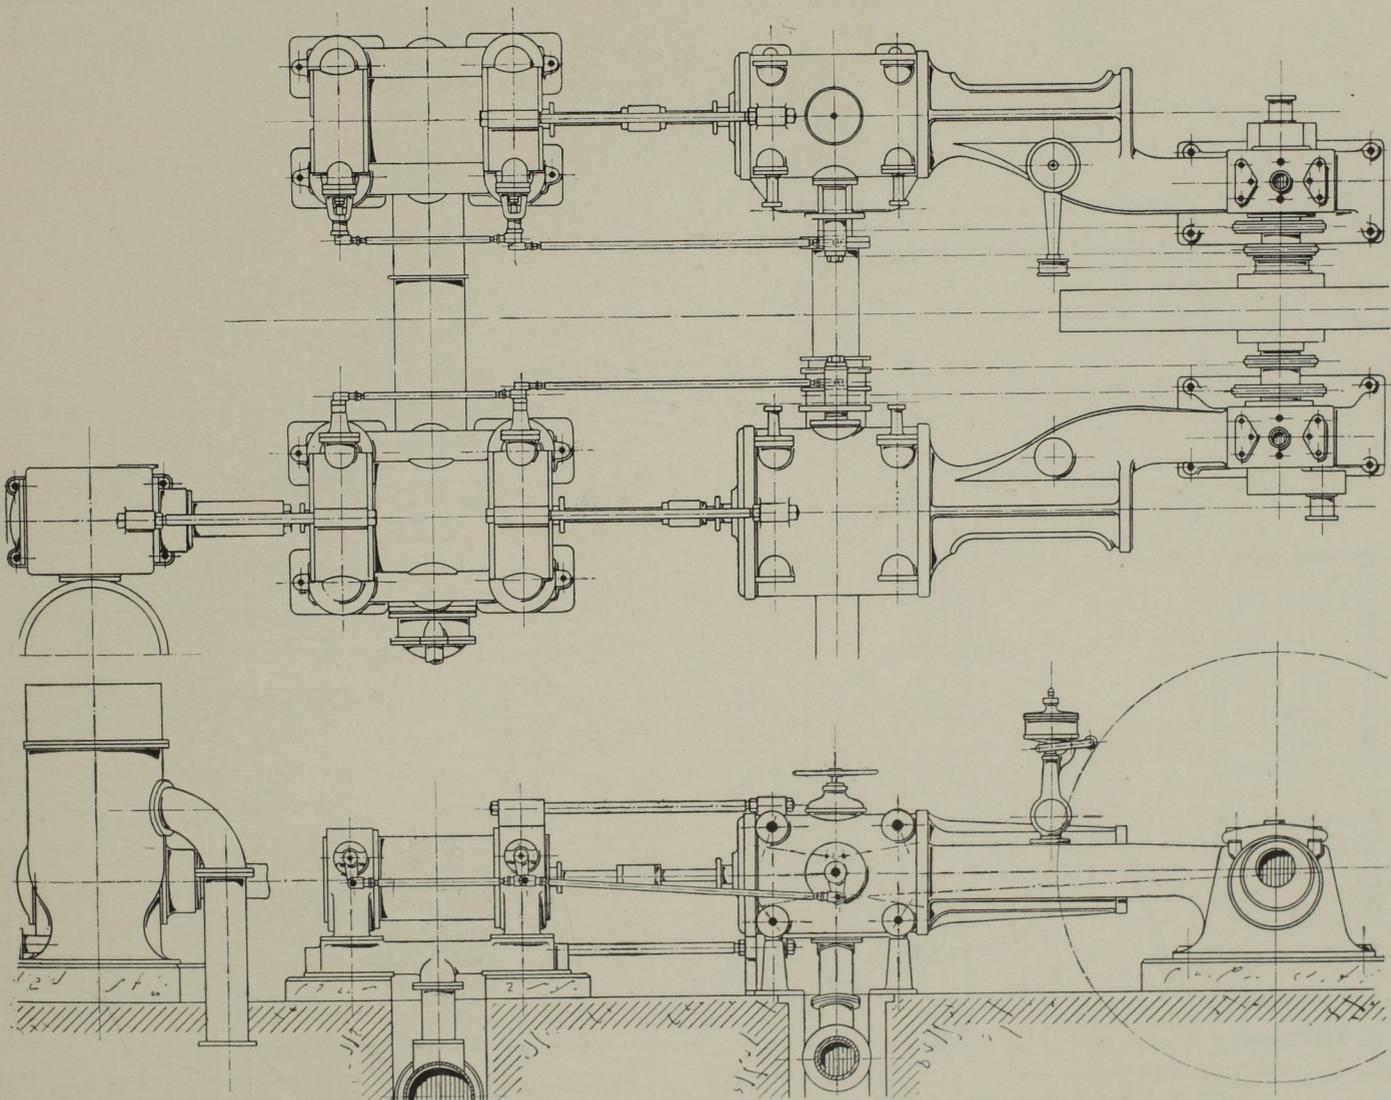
Grundriss und Aufriss des Kompressors. Masst. 1:48.
